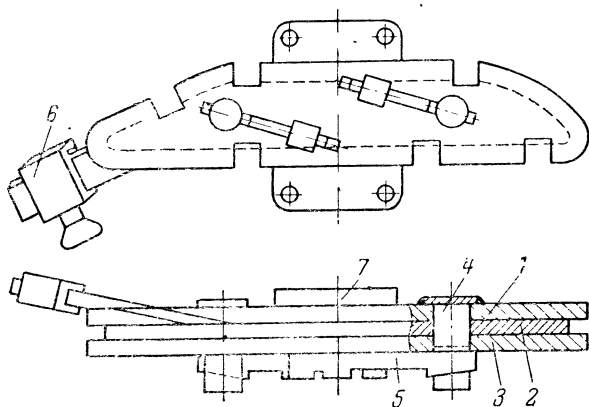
Шаблон-лодочка для намотки катушек двух-
